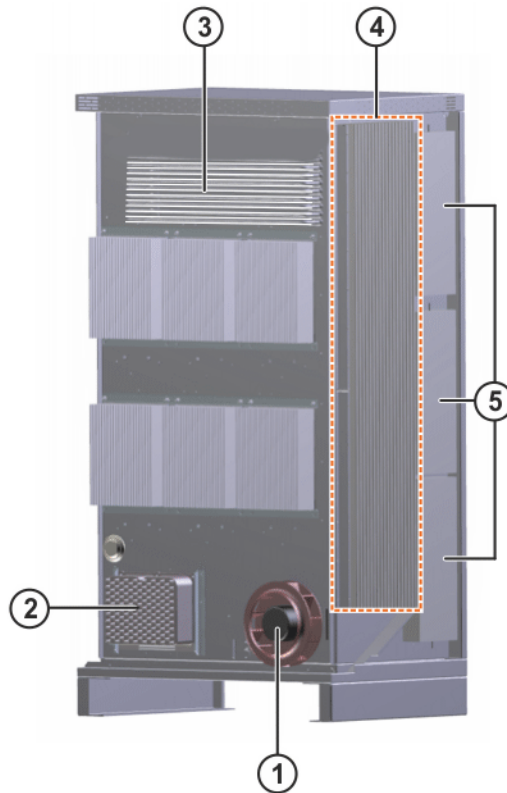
Aperçu de la commande de robot, vue arrière
